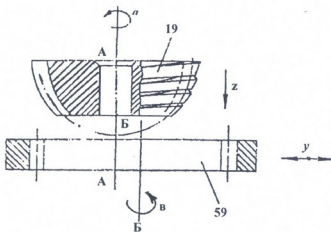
Схема нарезания некруглого цилиндрического колеса с внутренними зубьями
